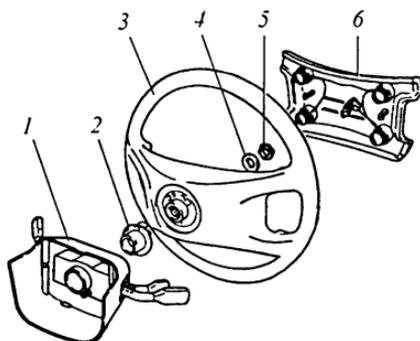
Демонтаж и установка рулевого колеса: 1 — выключатель на колонке рулевого управления с консолью; 2 — поводок со скользящим угольным контактом; 3 — рулевое колесо; 4 — пружинное кольцо; 5 — гайка; 6 — крышка
